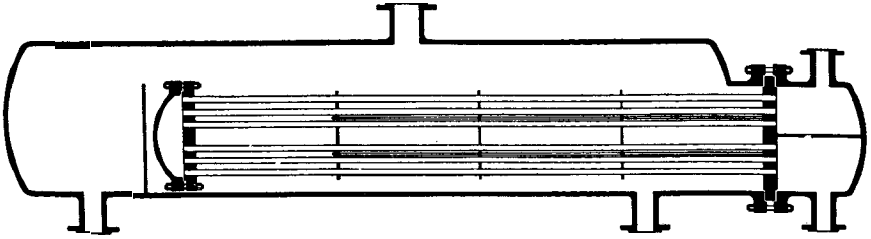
Caldereta tipo marmita. (*Patterson Foundry and Machine Co.*)
